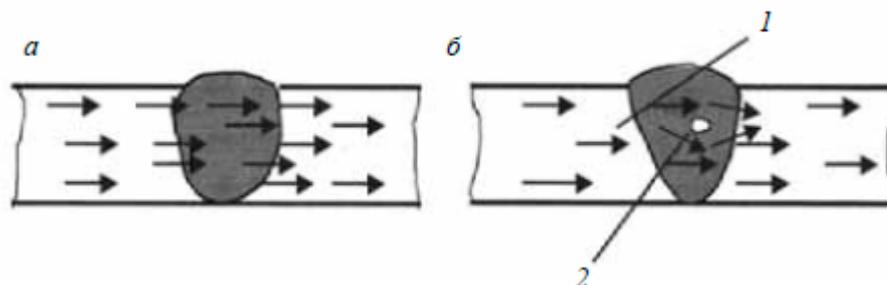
Схема прохождения магнитного потока в сварном соединении:
